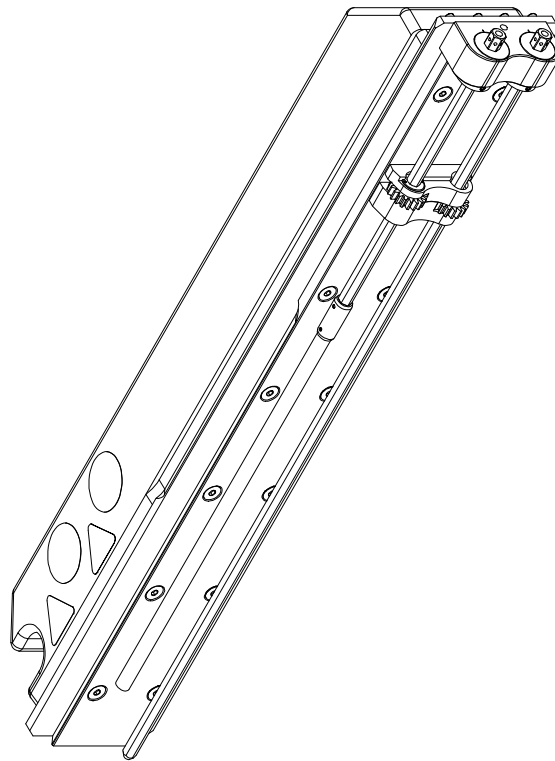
LISTE DE PIÈCES ENSEMBLE BRAS D'USINAGE (P/N 90337 RÉVISION E)
